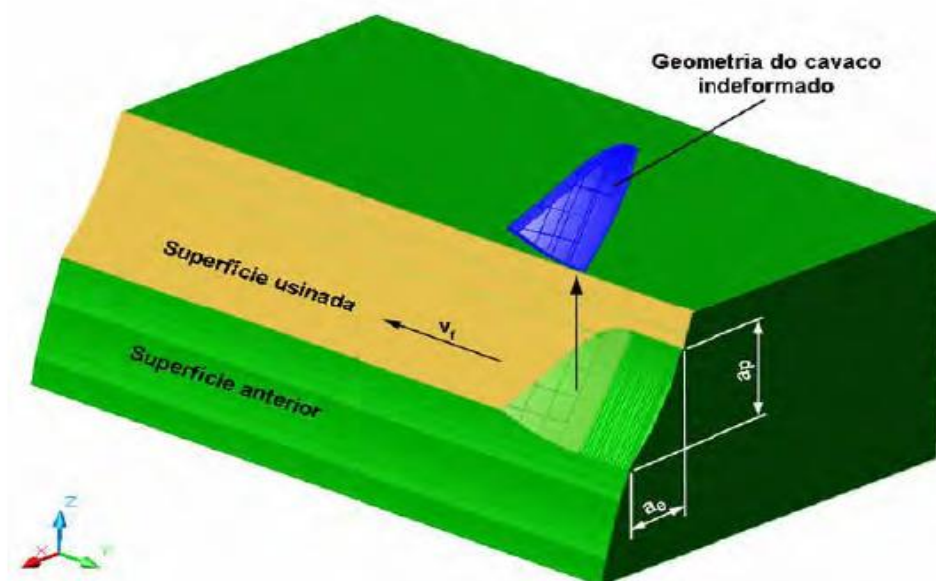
Geometria do corte com ferramenta esférica ou toroidal.
